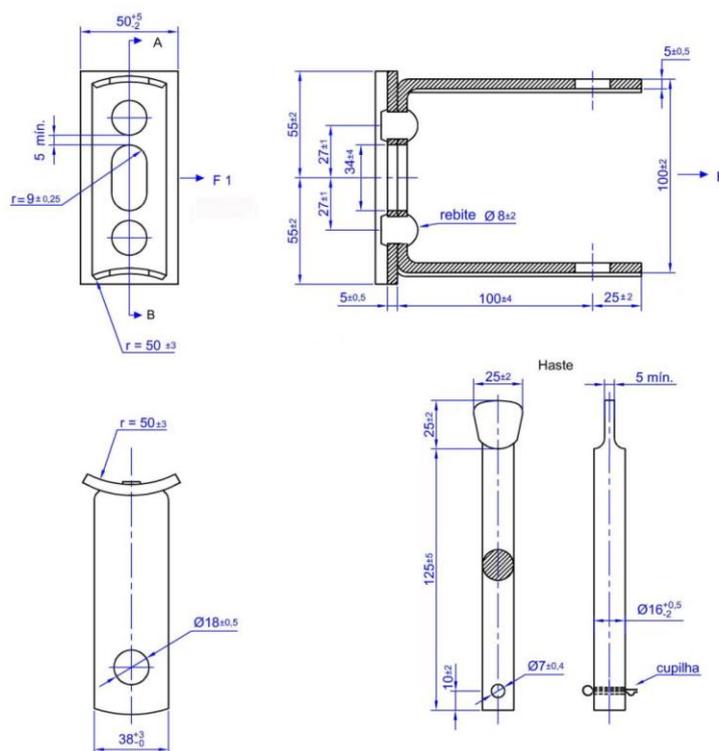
Dimensões Armação Secundária um estribo e aplicação das forças F e F1.
